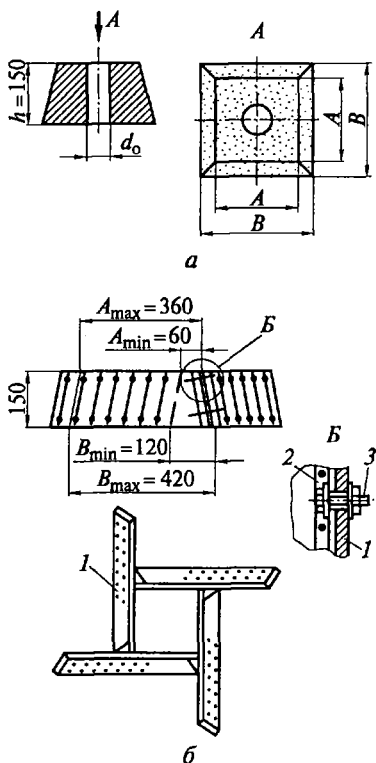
Безопочная форма-проба (а) и разборная опока (б) для изготовления формы-пробы:
